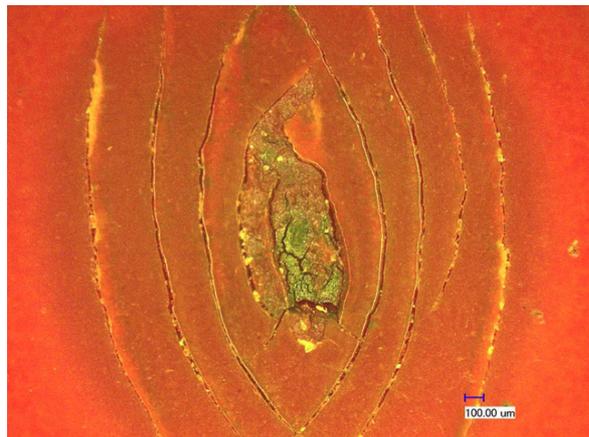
Risse in Beschichtung der Farbübertragswalze, verursacht durch Metallteilchen
